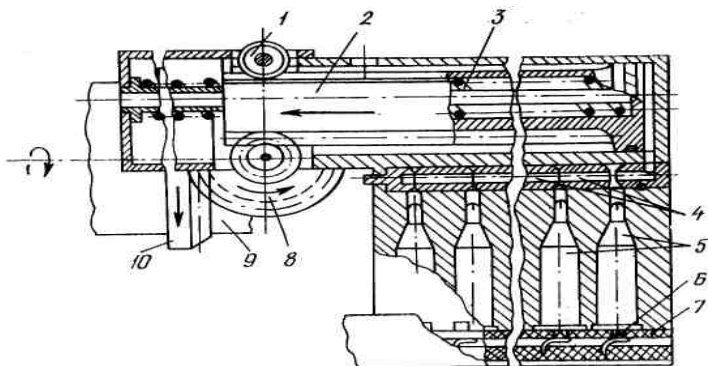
Конструктивна схема стартера гармати ГШ-6-23
